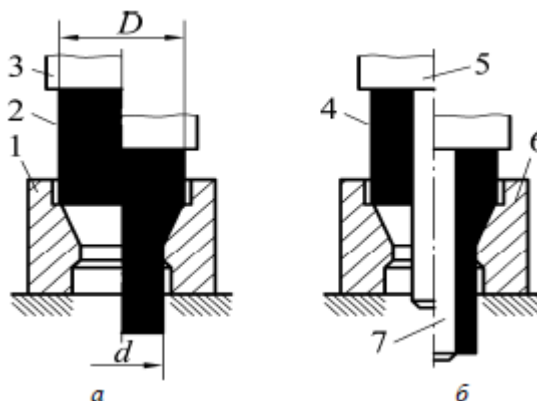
Схемы редуцирования сплошной (а) и полой (б) заготовок: 1, 6 – матрицы; 2, 4 – заготовки; 3, 5 – пуансоны; 7 – оправка; D , d – диаметры заготовки до и после редуцирования
